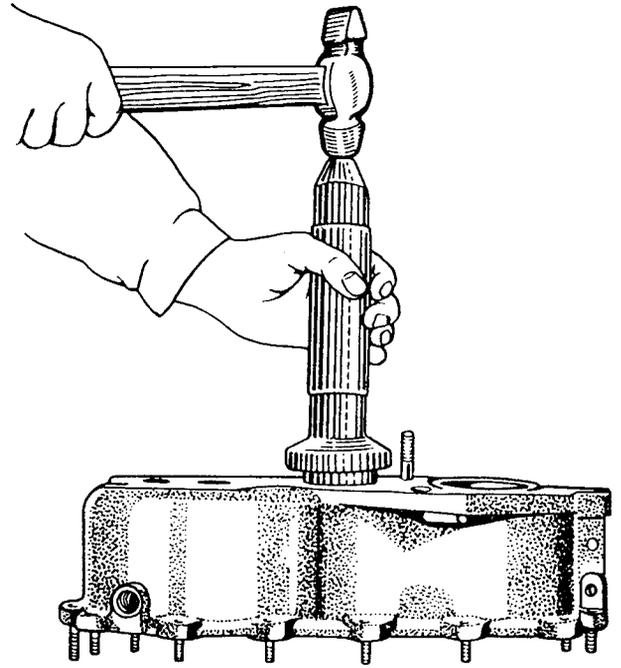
Einpressen des Rollenlagers in das Gehäuse
